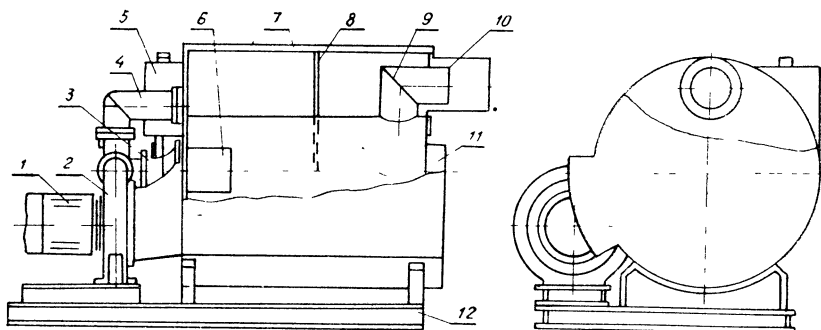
Газовоздушный подогреватель ГОСНИТИ:
